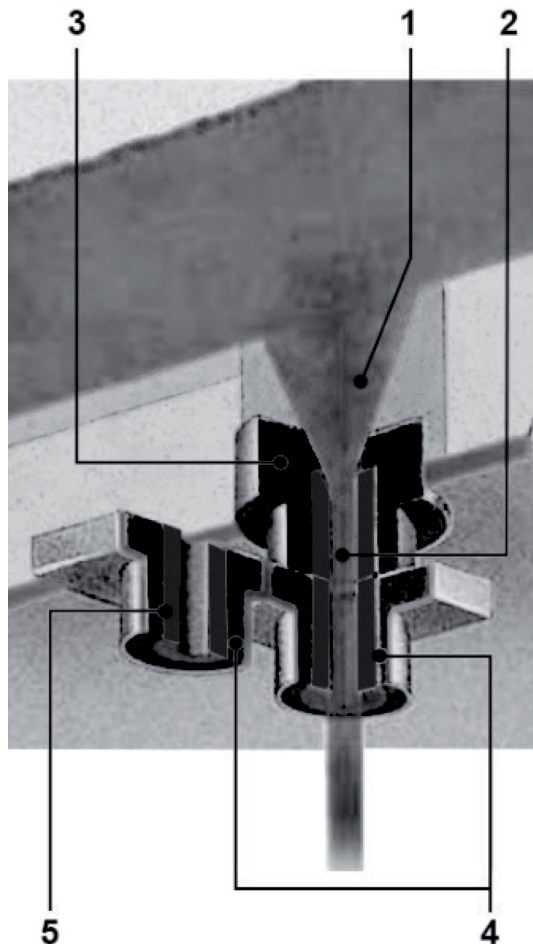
Принципиальная схема быстрой замены стаканов-дозаторов промежуточного ковша сортовой МНЛЗ: 1 – воронка из набивной массы или формованный гнездовой блок; 2 – калиброванная струя металла; 3 – верхний стакан-дозатор типовой конструкции; 4 – нижний (сменный) стакан-дозатор; 5 – ZrO_2 -вставка стакана-дозатора
